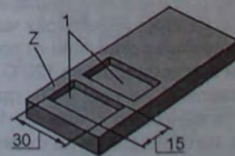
Модель для изготовления пластинчатых образцов КО
